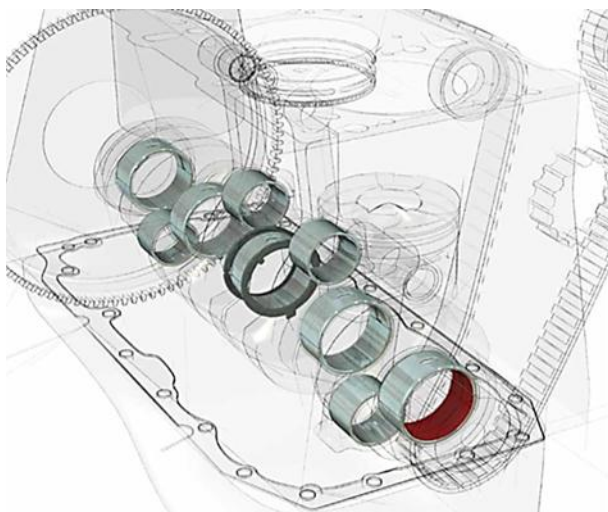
Расположение подшипников скольжения опорного вала в двигателе внутреннего сгорания [3]
